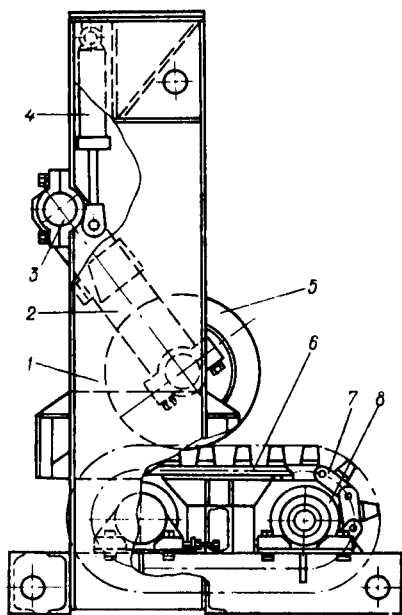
Схема регулирования исходного положения окорочной головки станка ОК100-2 и натяжения ремней:
